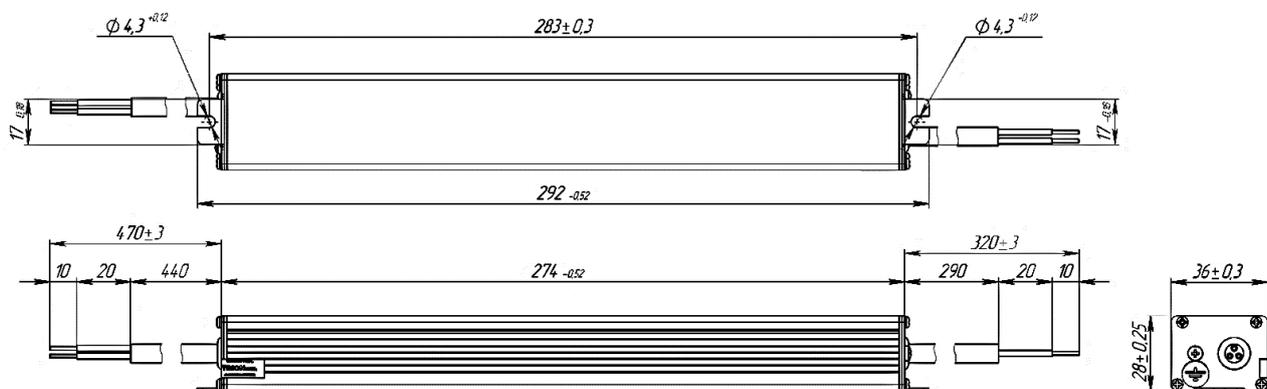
Габаритные размеры источников STAR 100-700T Industrial и STAR 130-700T Industrial
